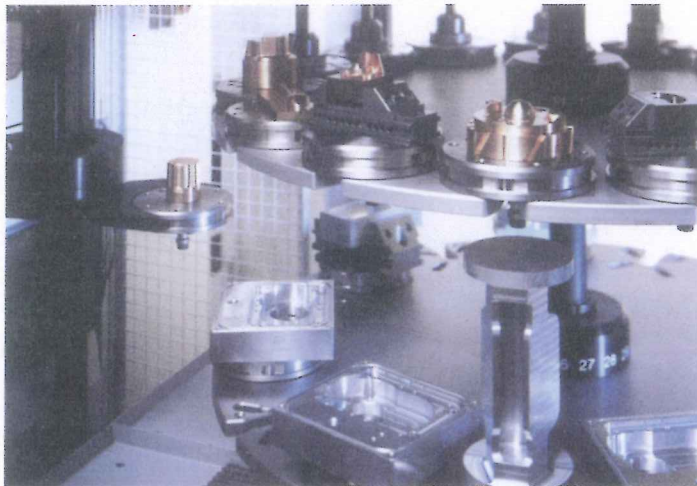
Magazin für bis zu 90 Werkstücke mit Handhabungsroboter zum unbeaufsichtigten Produzieren mit automatischem Werkstückwechsel
